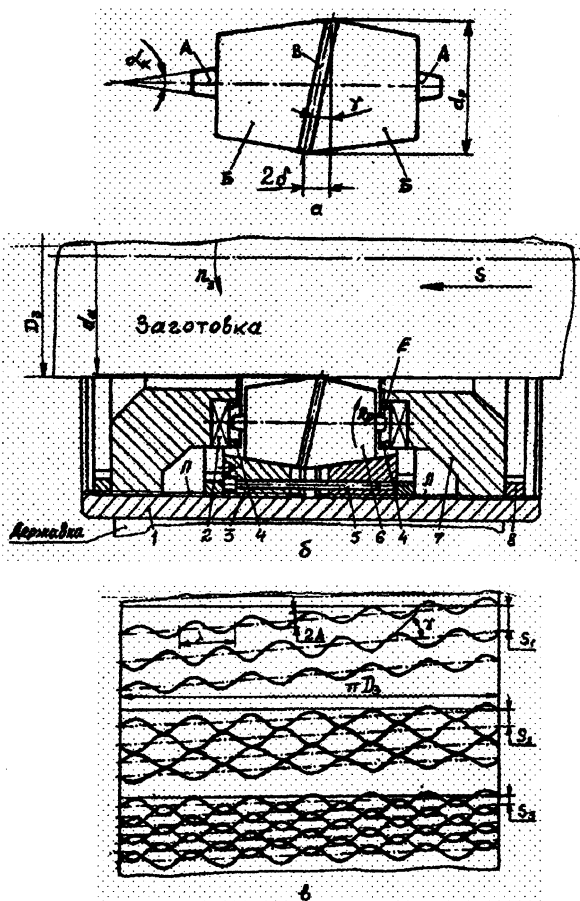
Высокопроизводительное переналаживаемое приспособление для совмещения обработки ППД: а — ролик, б — устройство, в — следы обработки с различными подачами
